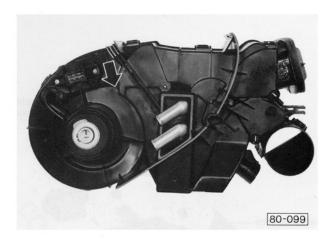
Befestigungsschraube der rechten Gehäusehälfte (Pfeil) herausdrehen
